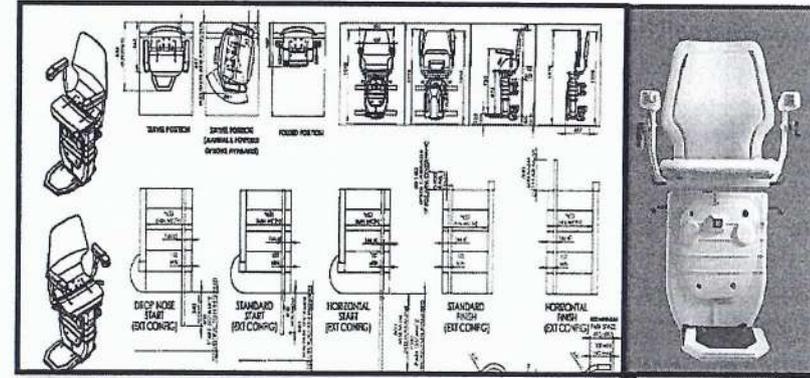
Plano técnico e imagen de referencia silla Salvaescalera
